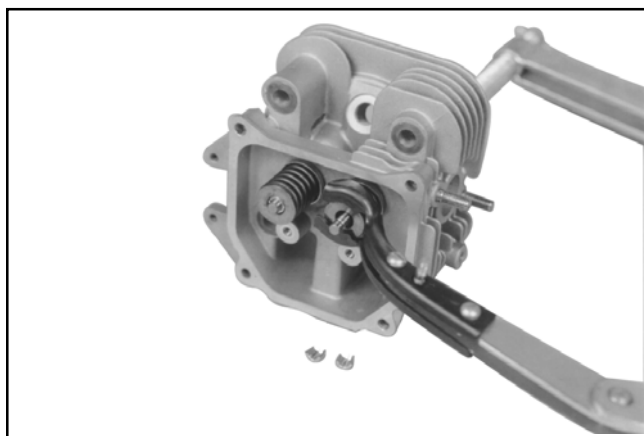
Rimozione delle valvole con il compressore per molle delle valvole.
